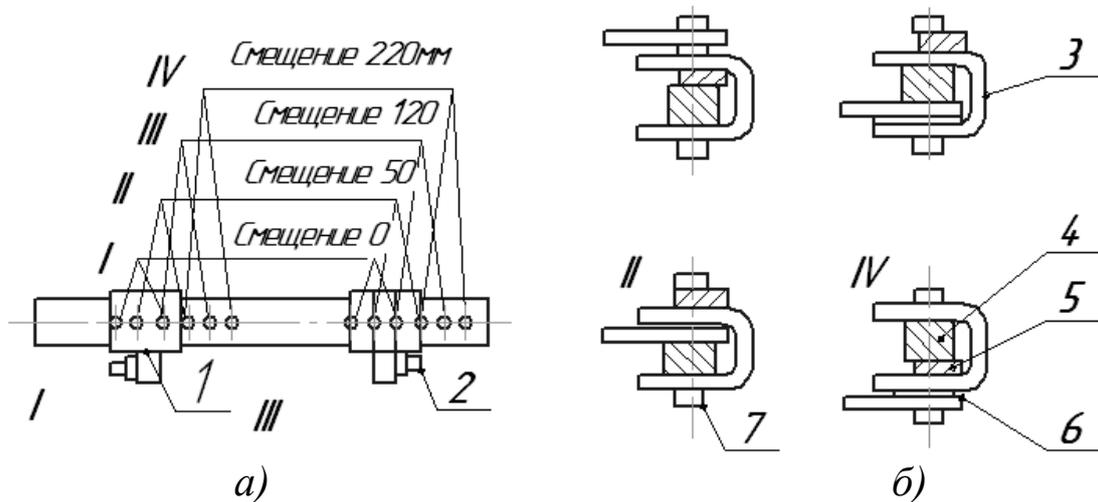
Схемы установки: а) кронштейнов на поперечной балке рамы; б) штока догрузителя
